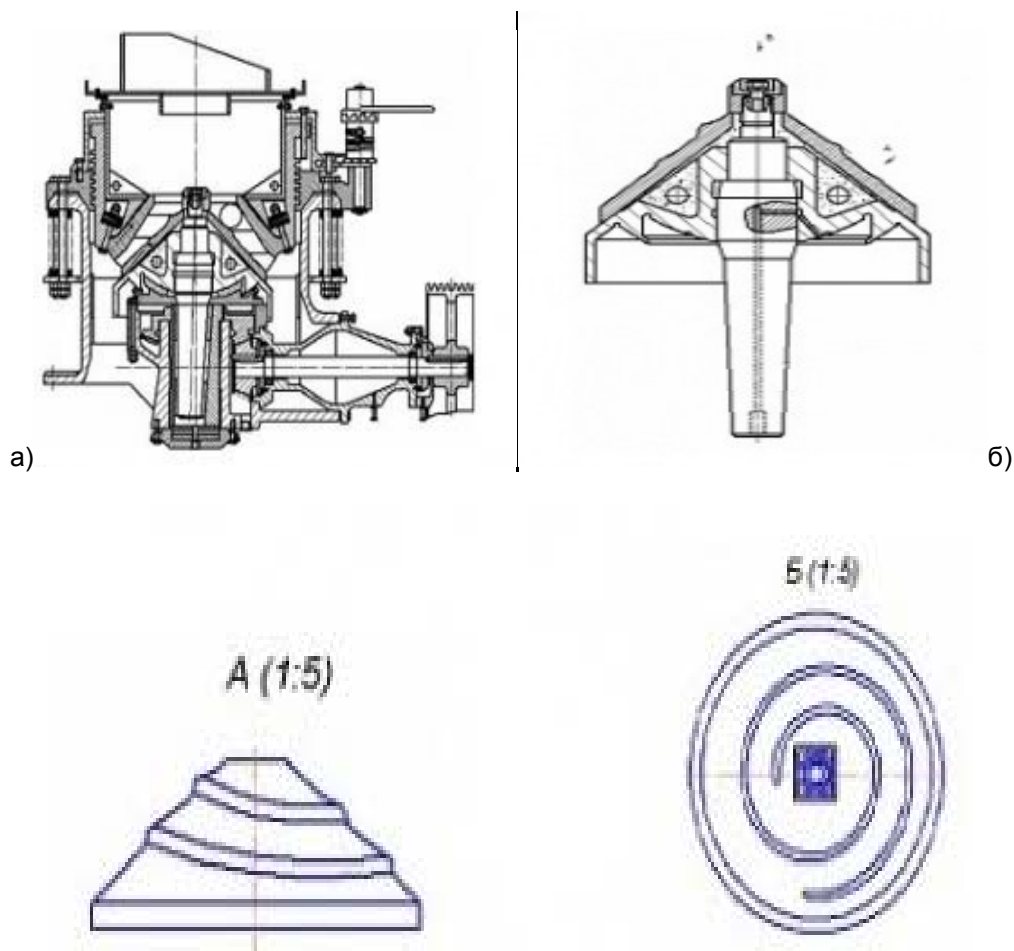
Конусная дробилка для получения кубовидного щебня:
